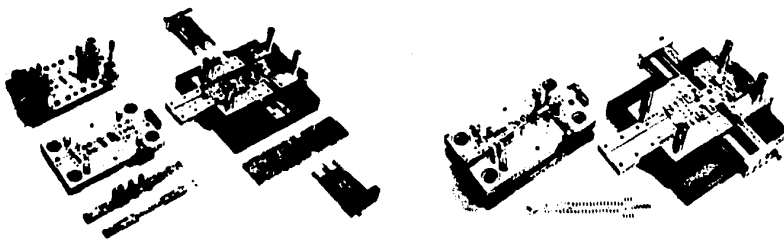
A. MATRIZ PROGRESIVA Y COMBINADA VISTA EN DESPIECE (IZQUIERDA) Y MONTADA (DERECHA).
